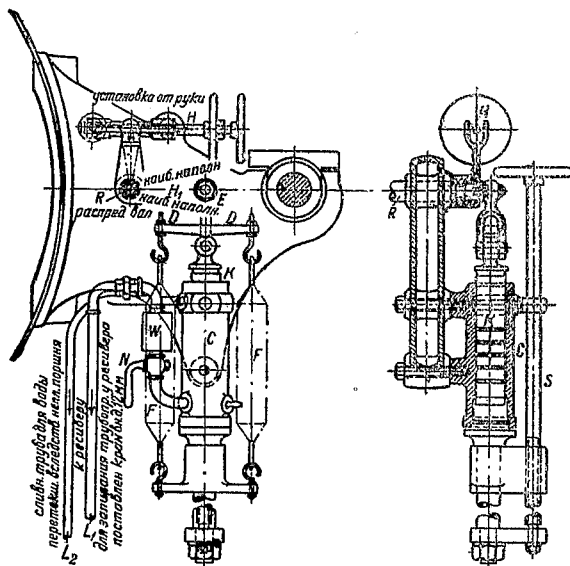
Регулятор давления промежуточного отбора пара с приспособлением для его изменения.
